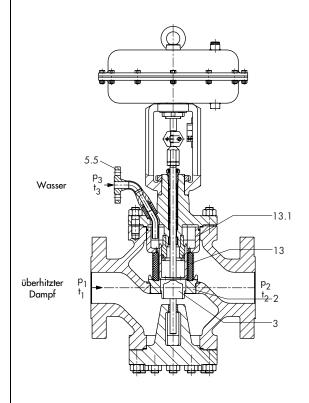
· Pneumatischer Dampfumformer Typ 284-1 mit Flanschen und druckentlastetem Ventilkegel
